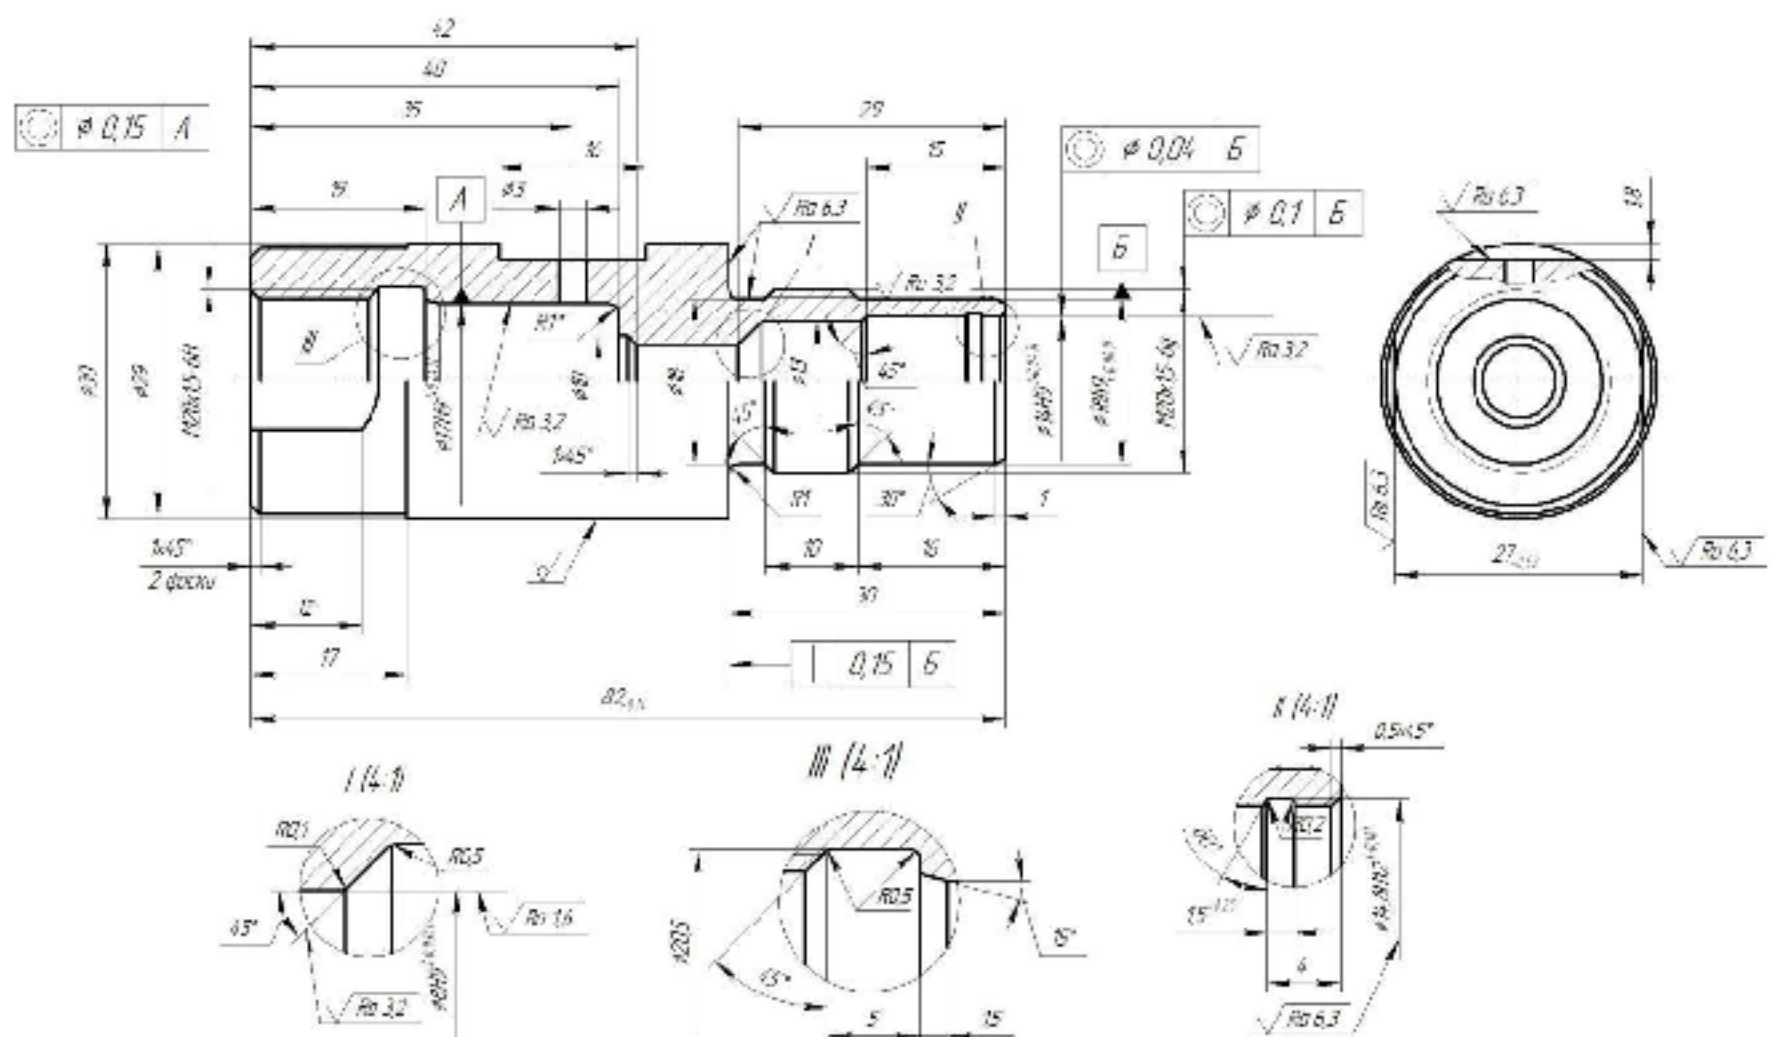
Креслення деталі «Корпус клапана 12.01.004»
